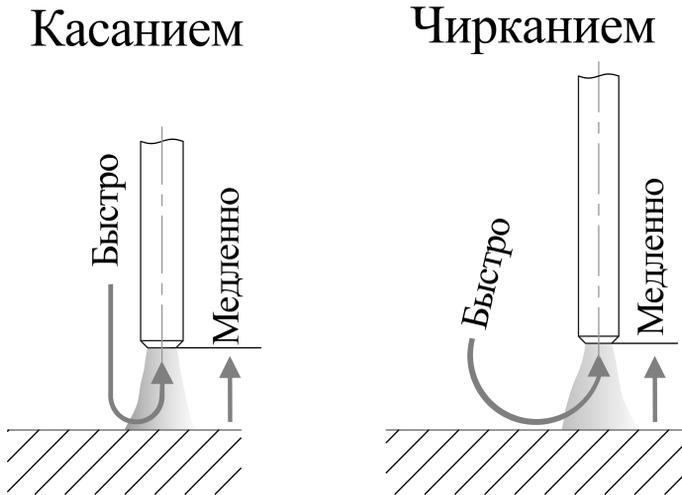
Способы зажигания сварочной дуги.
